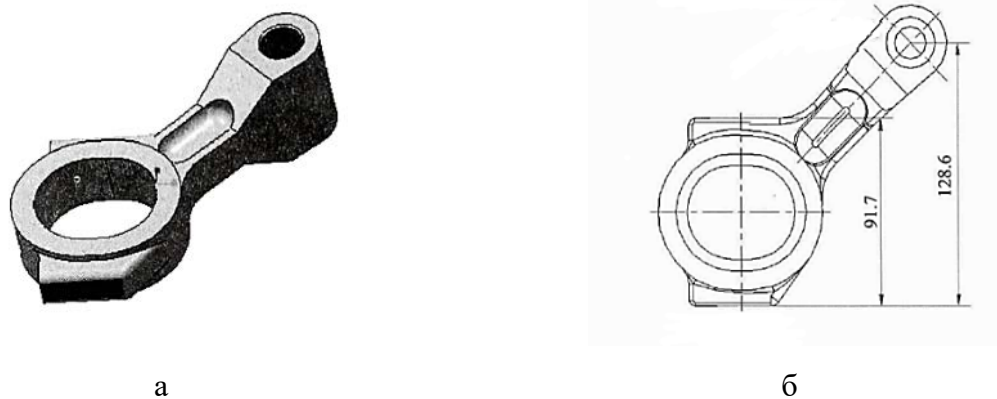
Поковка шатуна (а) и базовые поверхности (б)
